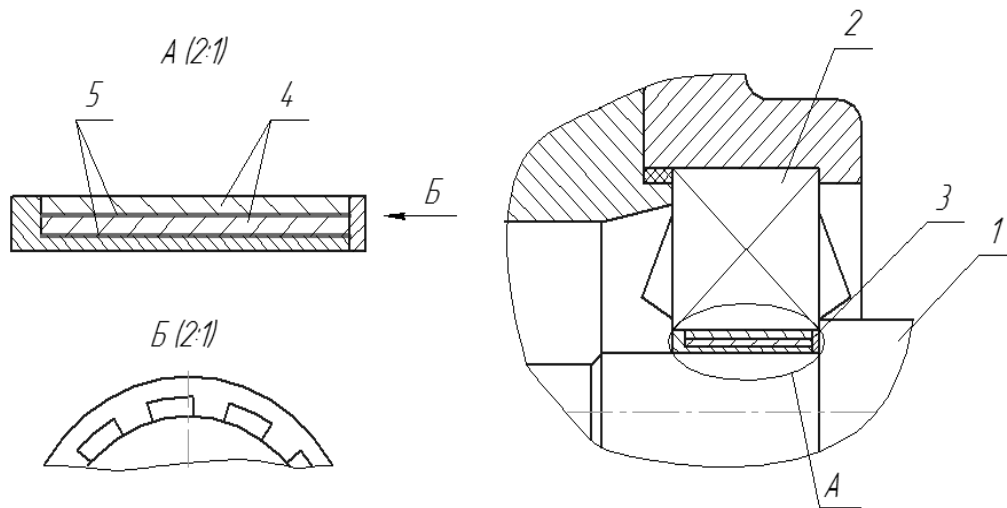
Схема улаштування підшипника роликоопори на її вісь
